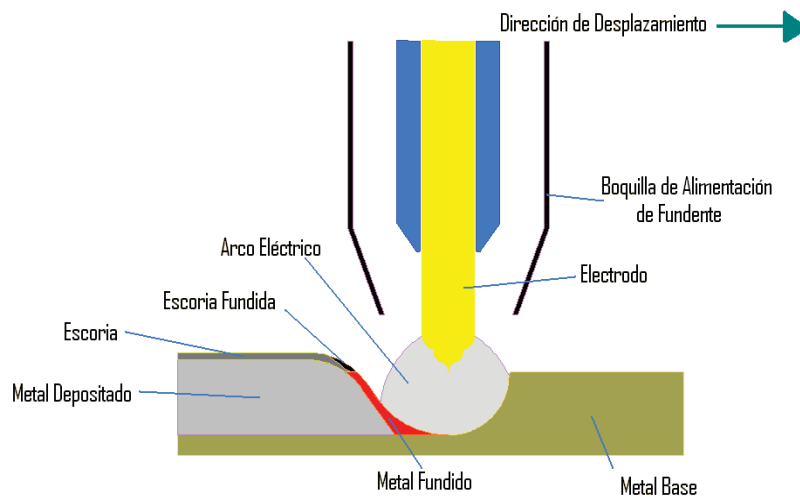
Descripción gráfica del proceso de soldadura SAW [2].
